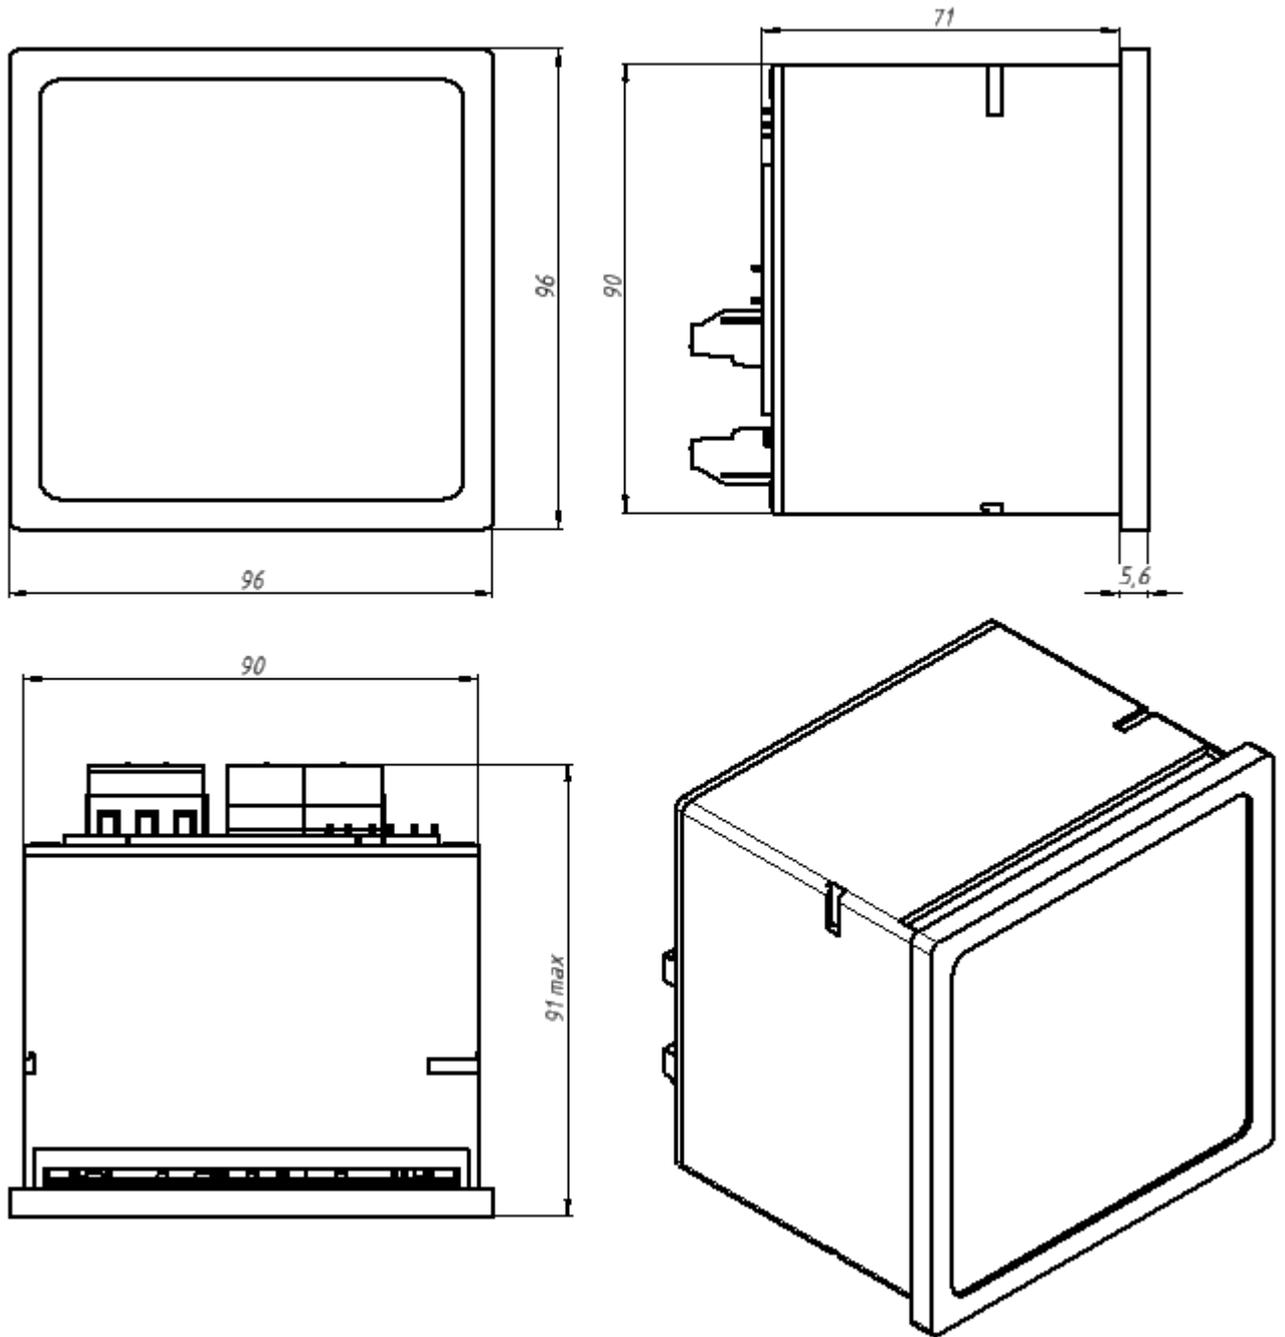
Габаритные размеры РЗЧФ-1001
